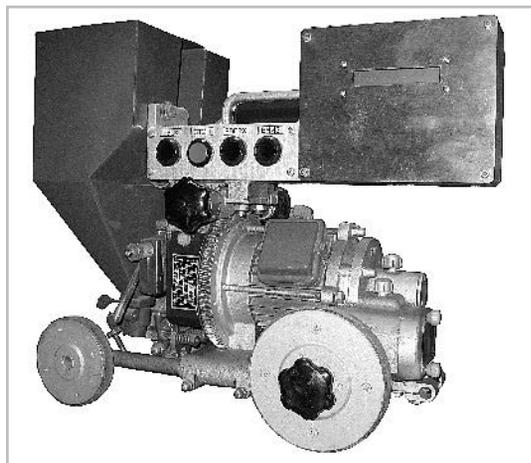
Сварочный автомат АДФ-1002Ц с цифровым управлением
